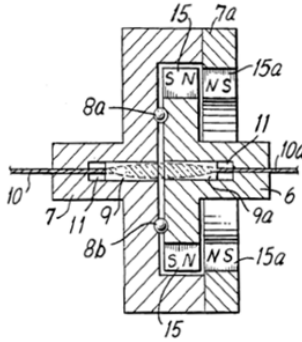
Волоконно-оптический поворотный соединитель с постоянными магнитами
